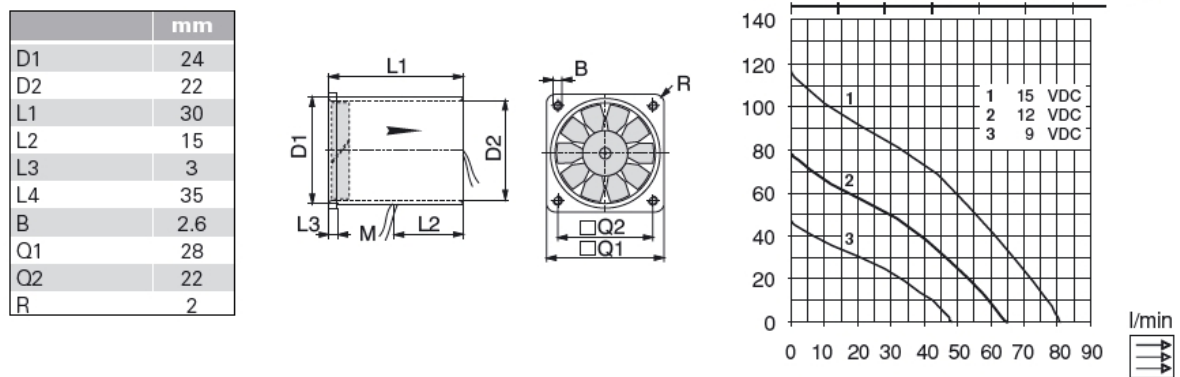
Kenndaten des 12 V Axialventilators: Technische Daten (links), Technische Zeichnungen der Seiten- und Vorderansicht (mitte), Kennlinie (rechts)
